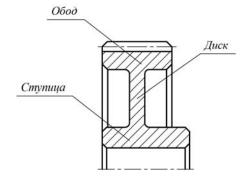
Конструктивные элементы зубчатого цилиндрического колеса
